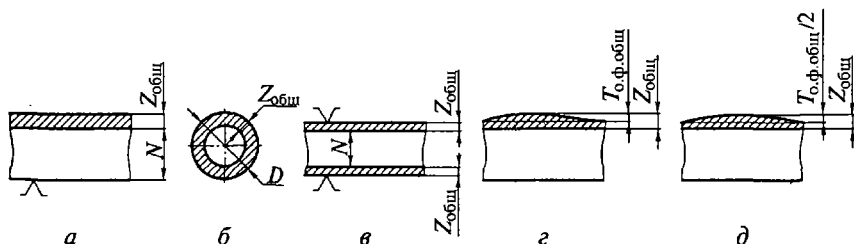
Варианты (а—д) назначения общего допуска для механической обработки:
